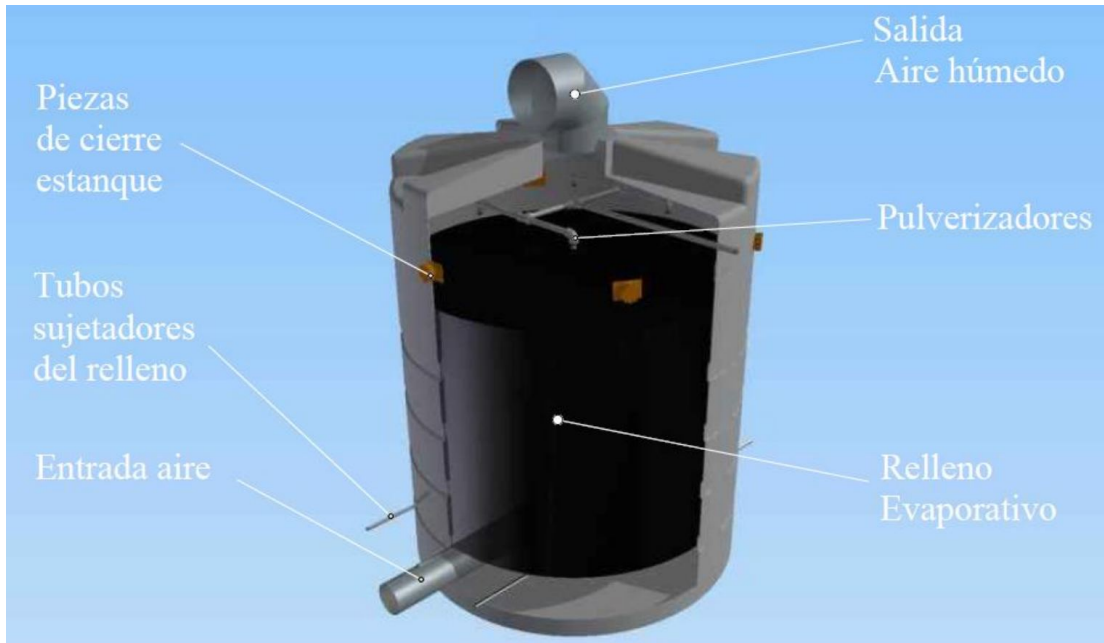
Diseño del humidificador completamente ensamblado. Fuente [28].
